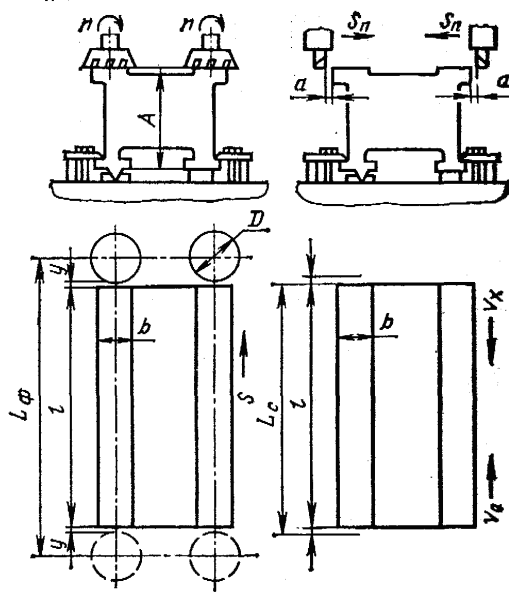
Обробка площини основи заготовки станини фрезеруванням і струганням
